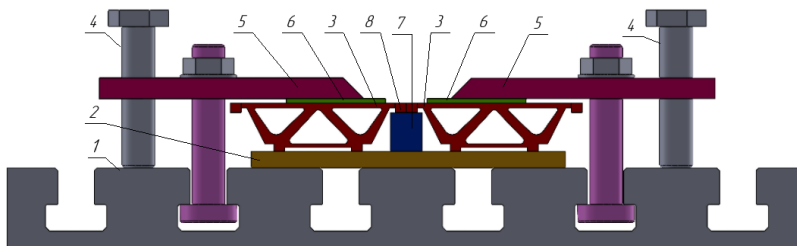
Получение стыкового сварного соединения при СТП двух панелей:
